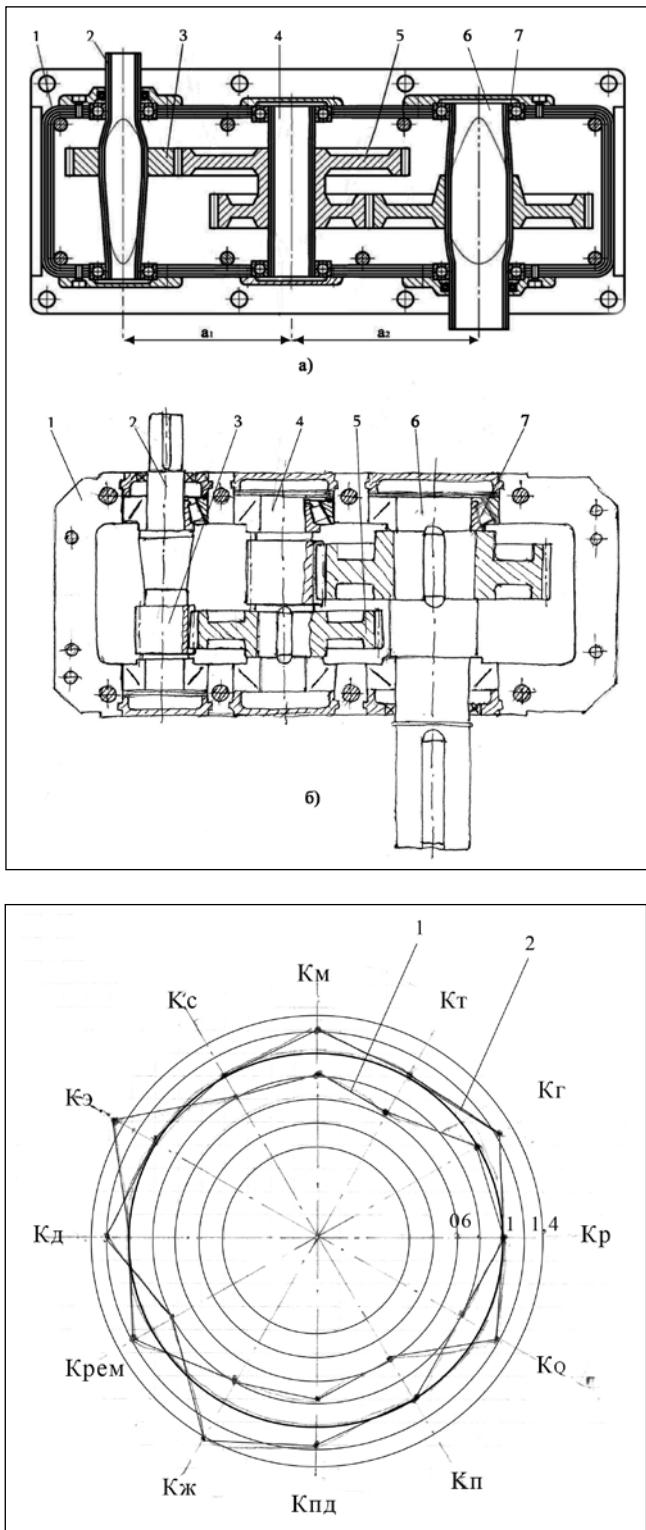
Двухступенчатые редукторы: а) эталонный, б) стандартный. 1 — корпус, 2 — вал, 3 — шестерня, 4 — промежуточный вал, 5 — зубчатое колесо, 6 — выходной вал, 7 — подшипник. a_1 и a_2 — межосевые расстояния с отрицательным допуском
